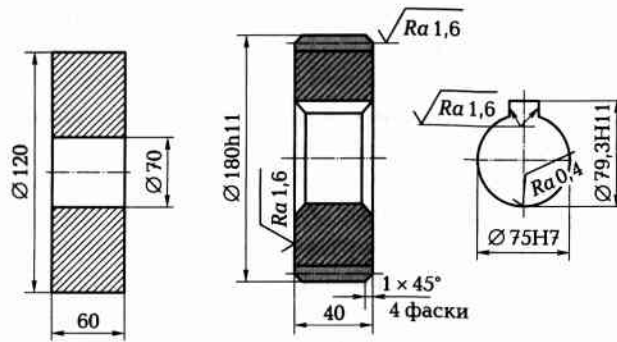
Обработка заготовки зубчатого колеса типа III
